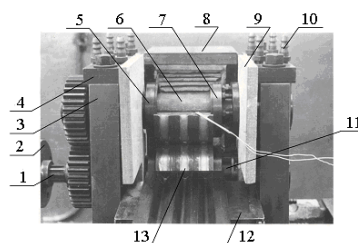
Установка для вальцювання в умовах ізотермічного деформування: 1 - шліцьове з'єднання, 2 - муфта, 3 - корпус, 4 - планка, 5 - нерухома шайба, 6 - верхня опора, 7 - рухома шайба, 8 - нагрівальний пристрій, 9 - термозахисний кожух, 10 - пристрій для охолодження, 11- приводний валець, 12 - проводка, 13 - вальцювальні штампи.
